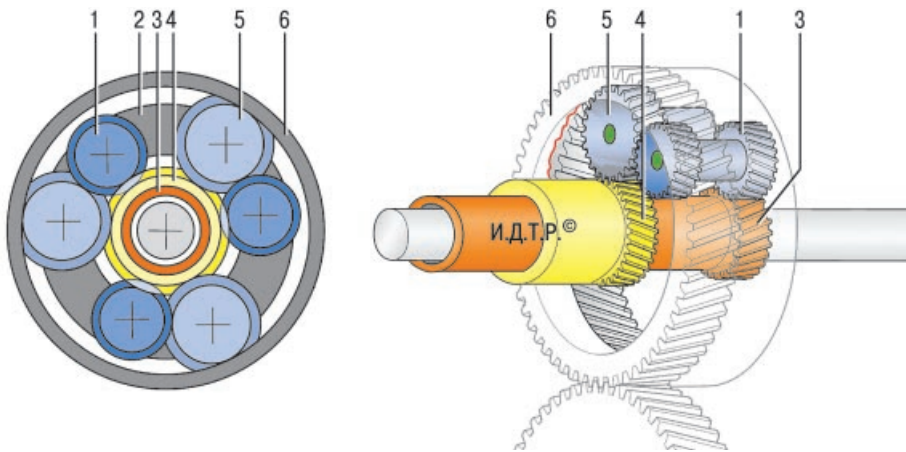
Планетарный редуктор системы Равинье: 1 – длинный сателлит; 2 – водило; 3 – малая солнечная шестерня; 4 – большая солнечная шестерня; 5 – короткий сателлит; 6 – коронная шестерня
